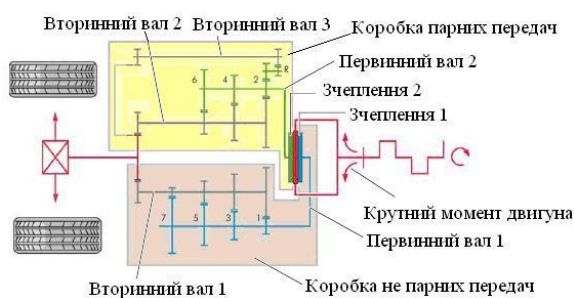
Принципова схема двопоточної коробки передач DSG [2]
